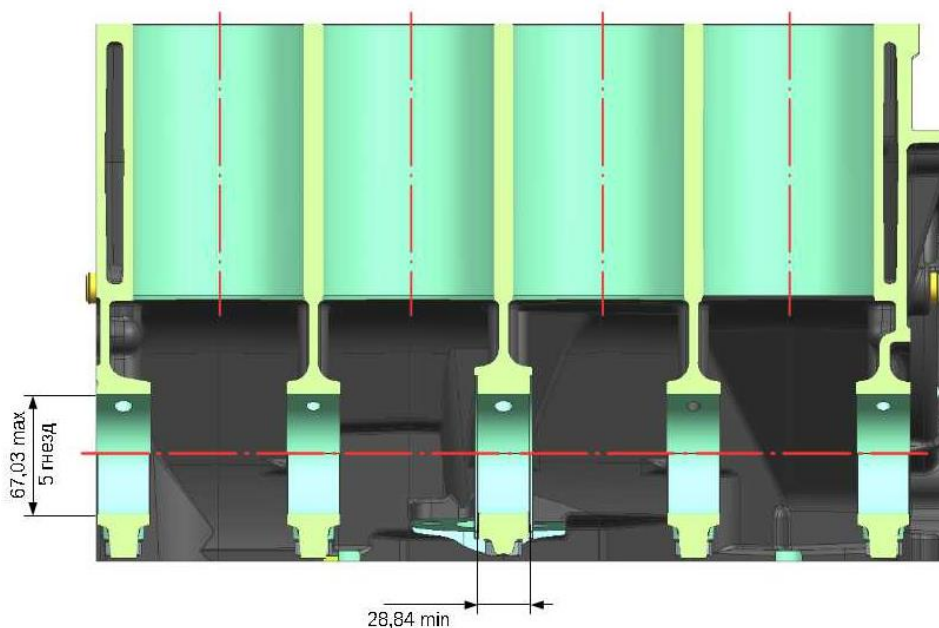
Предельные размеры цилиндров и гнезд коренных подшипников блока цилиндров
